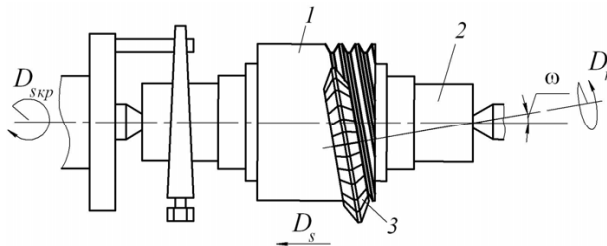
Схема фрезерования профиля червячной фрезы: 1 – заготовка фрезы; 2 – оправка; 3 – дисковая фреза
